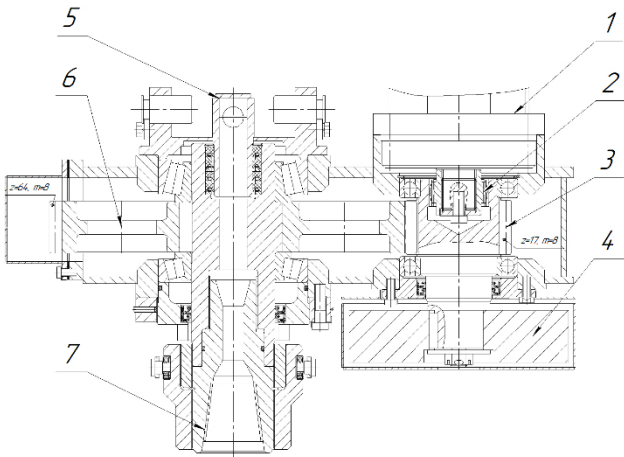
Одноступенчатый редуктор, применяемый в конструкции с использованием низкомоментного гидромотора и редуктора:
